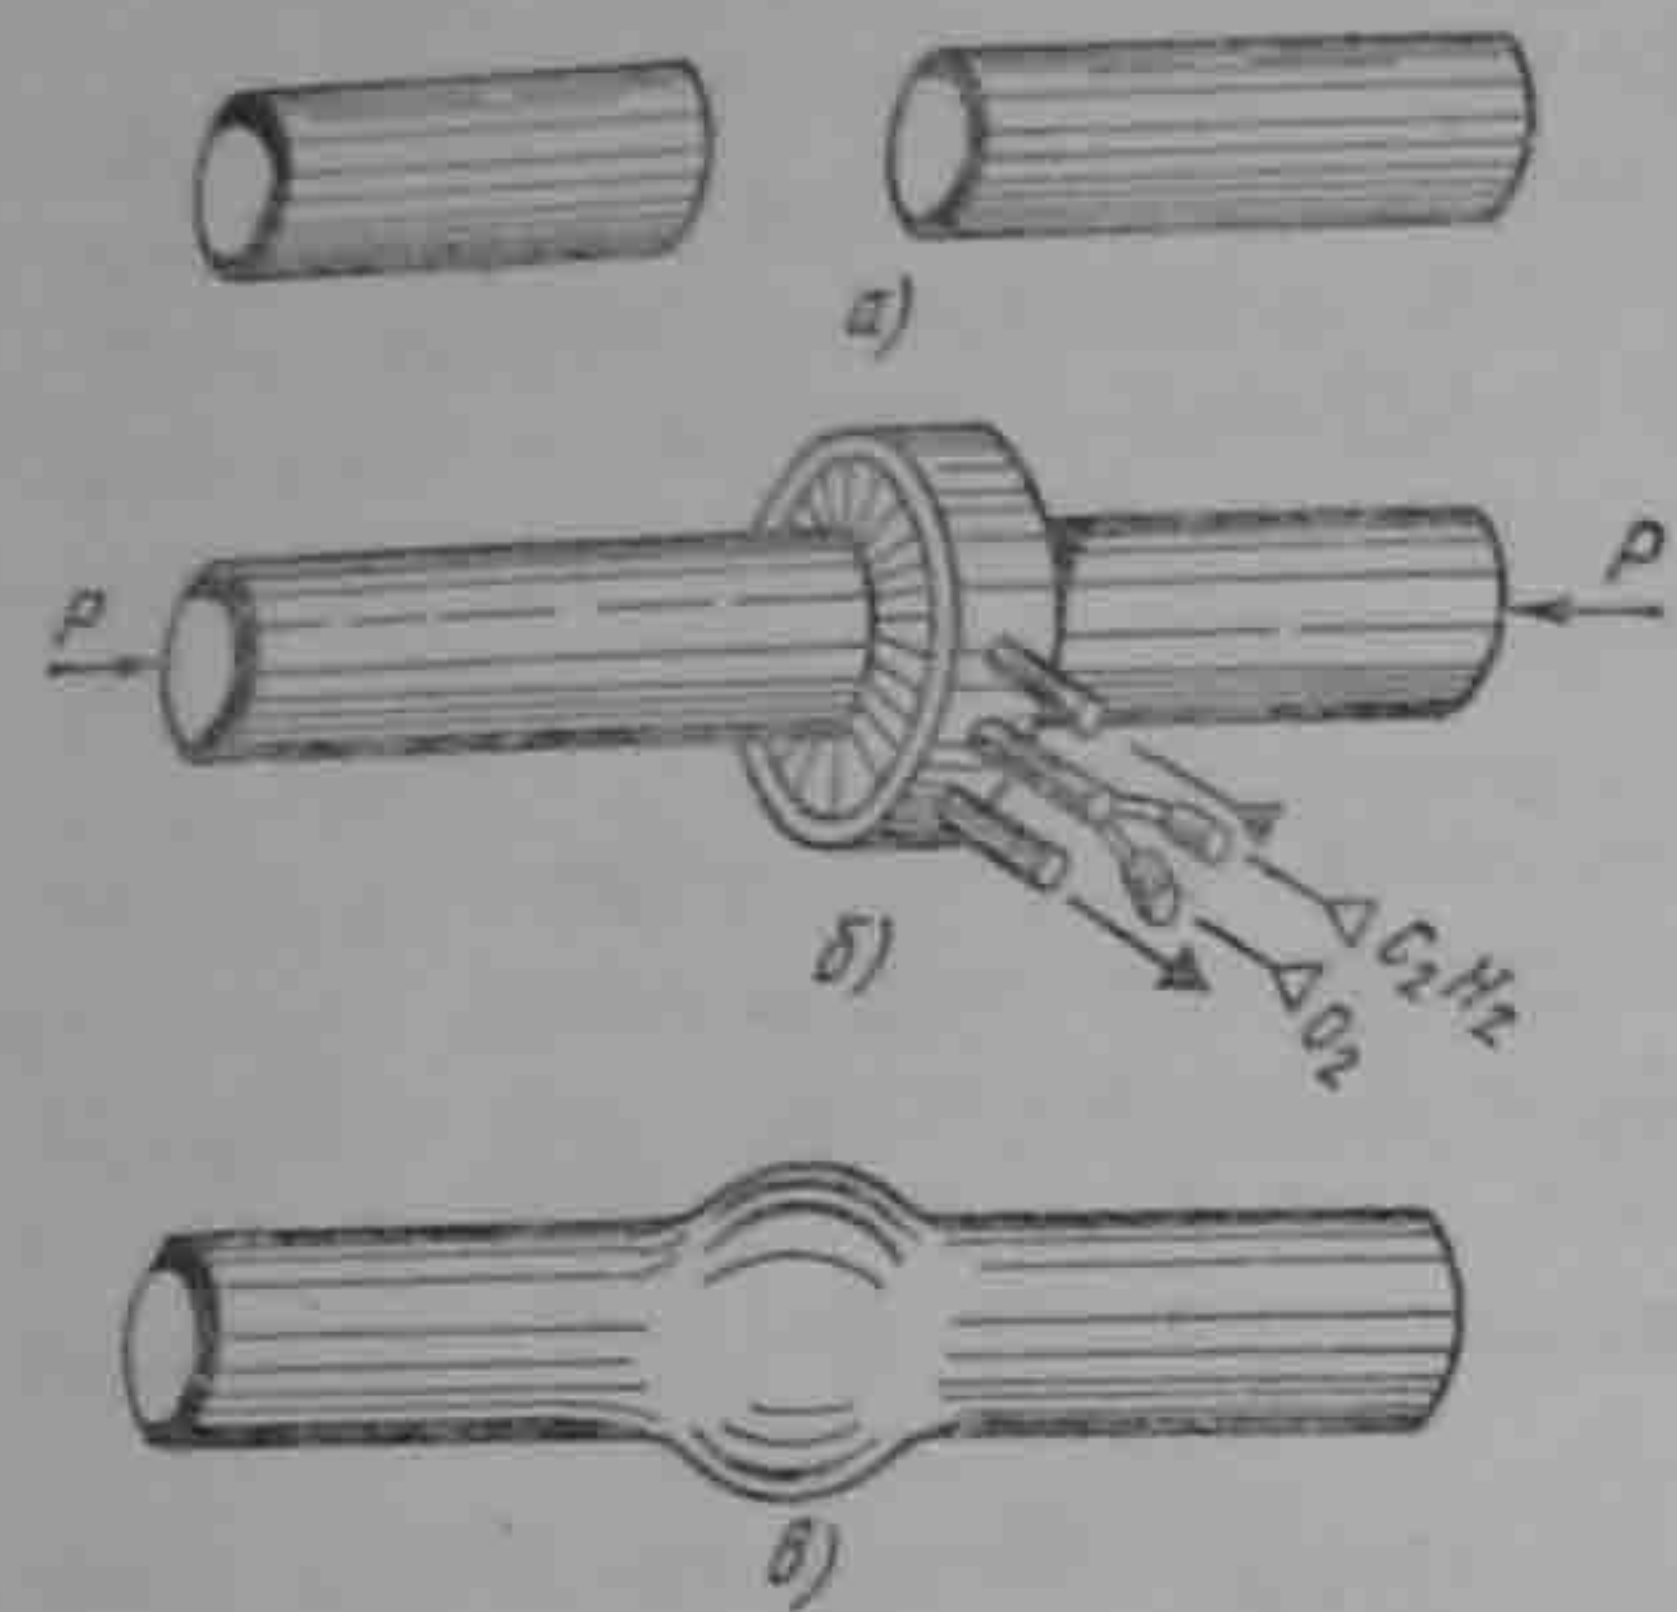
Принципиальная схема газопрессовой сварки:
